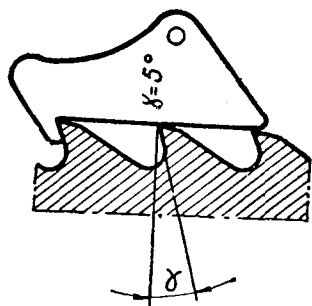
Шаблон для контроля переднего угла зуба протяжки
